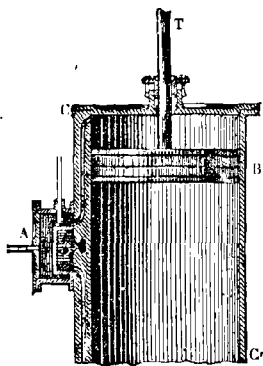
Coupe du cylindre et du piston d'une machine à vapeur.
